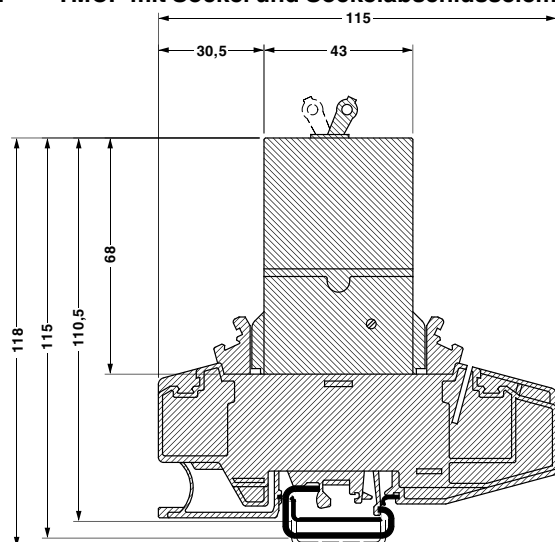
Maßbild mit Sockel (Abmessungen in mm)
